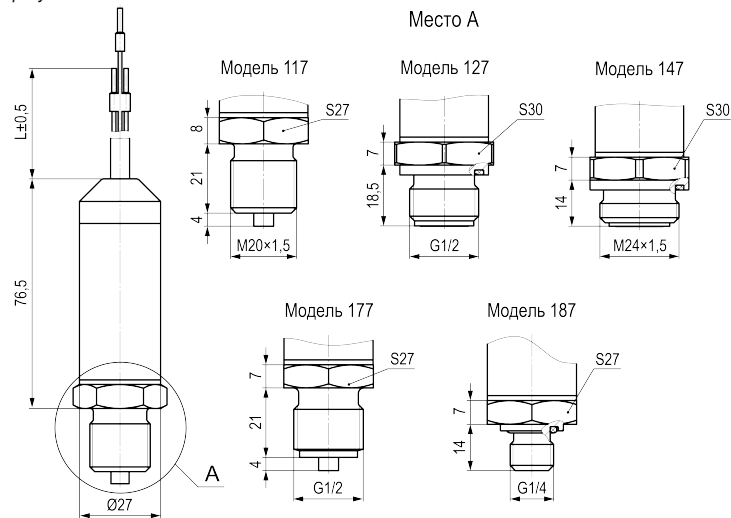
Габаритные и присоединительные размеры ПД100И-1Х7
